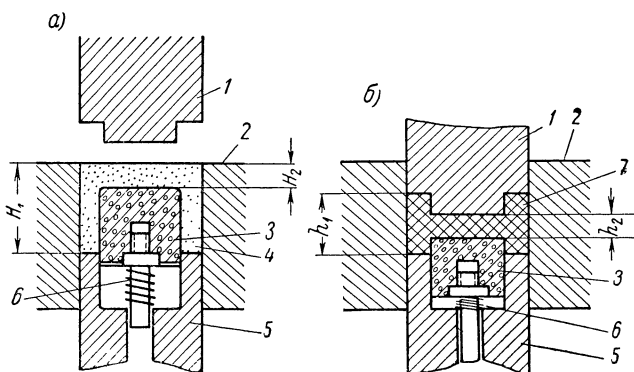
Схема прессформы с дифференциальной засыпкой для прессования заготовок боочных конденсаторов: а — в момент засыпки; б — в момент прессования.
